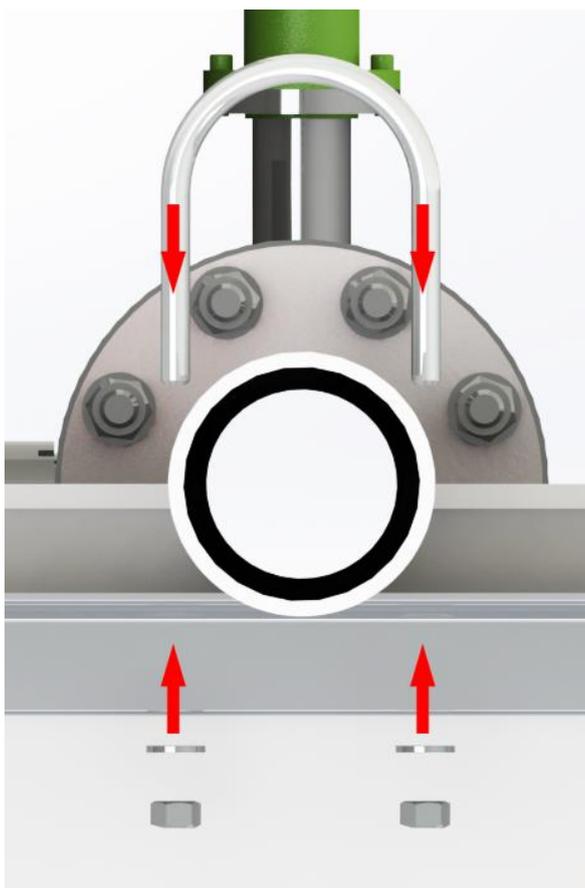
Установка хомута крепления к трубопроводу.
